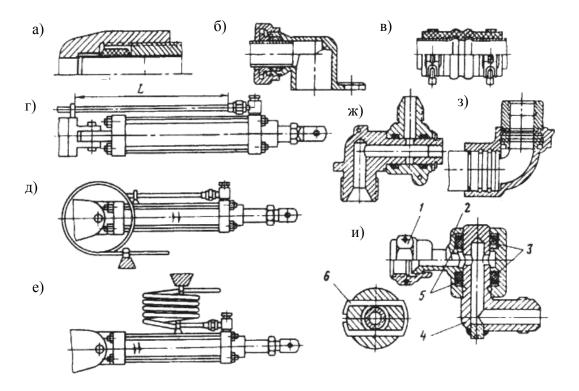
Схемы разъемных подвижных соединений трубопроводов: а – с уплотнительными кольцами; б – с телескопическими соединениями; в – с дюритовой муфтой; г – пружинного типа; д – со спиральной пружиной; е – с цилиндрической пружиной; ж, з – шарнирные соединения с одной и двумя степенями свободы соответственно; и – поворотные соединения: 1 – обжимная гайка; 2 – муфта; 3 – уплотнительное кольцо; 4 – угольник; 5 – защитная шайба; 6 – шпилька
